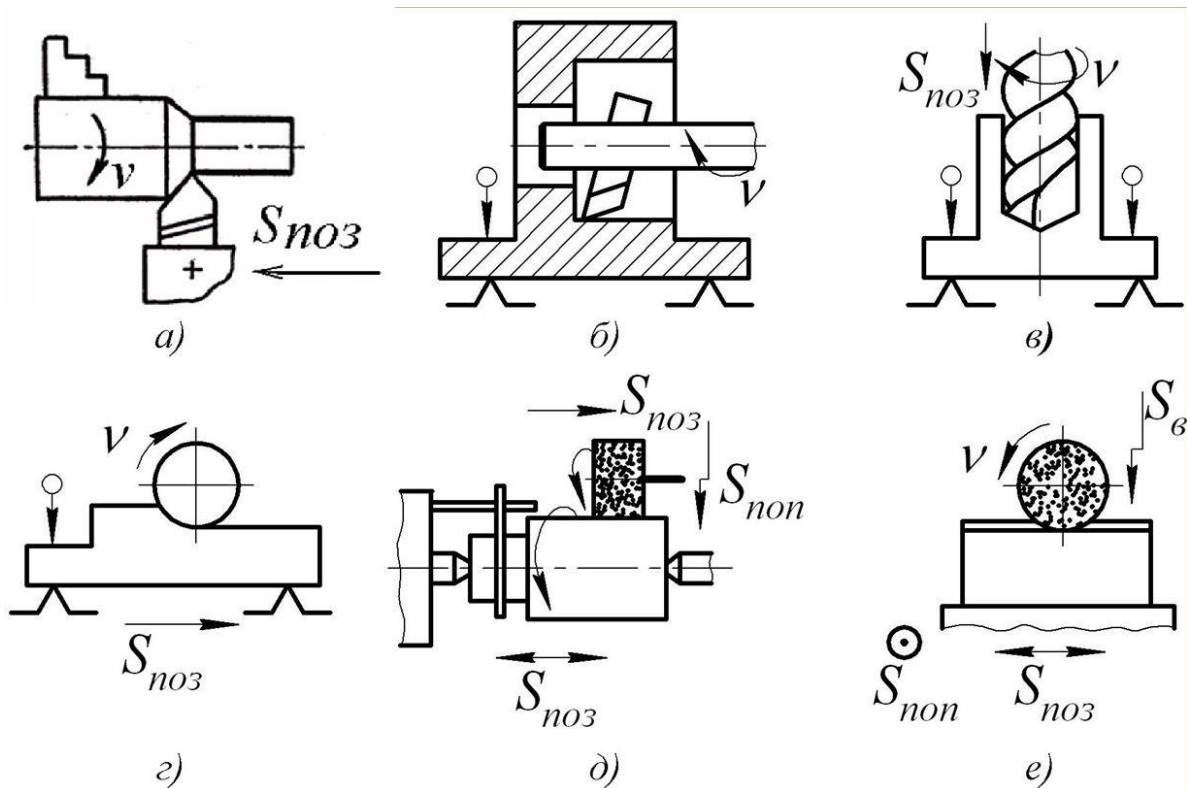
Схеми обробки заготовок: а - точінням; б - розточуванням; в - свердлінням; г - фрезеруванням; д - шліфуванням на круглошліфувальному верстаті; е - шліфуванням на плоскошліфувальному верстаті
